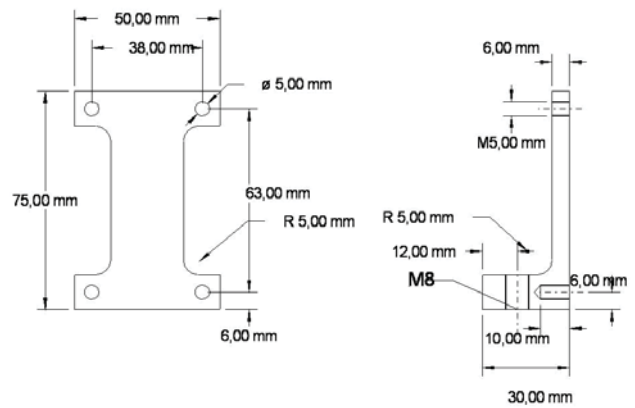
Supporteinheit der Schweißprobenkonfiguration B
